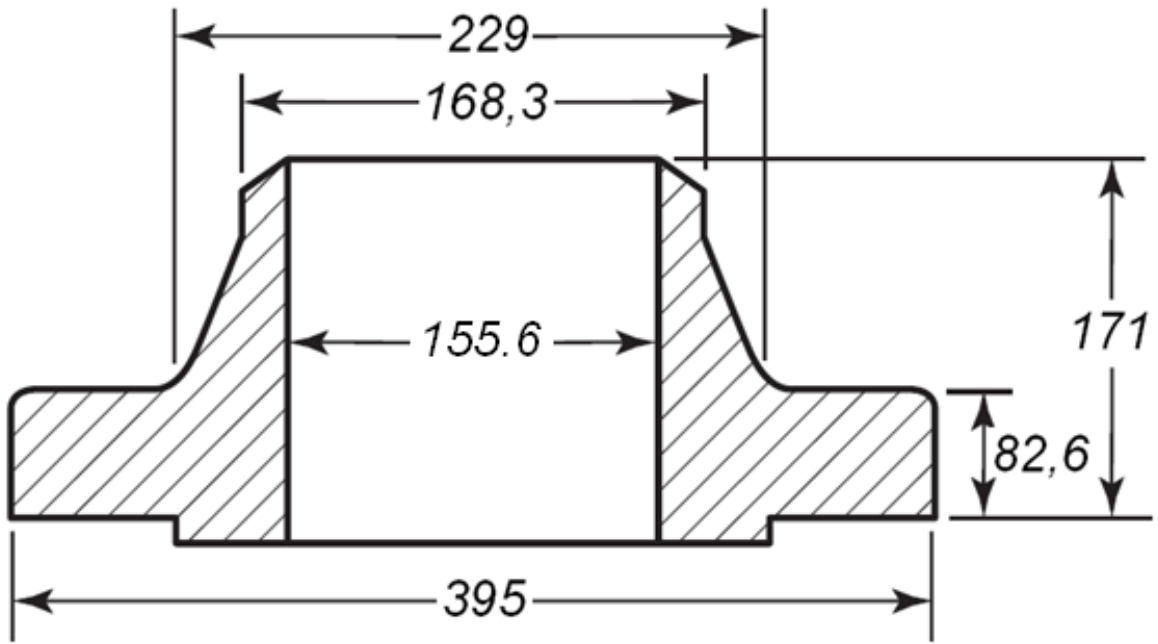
Dimensiones Welding Neck 6" Clase ASME 1500 [8]
